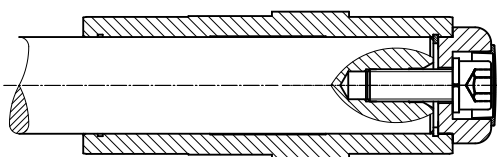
Крепление редуктора к валу без упора с помощью крепежного узла
